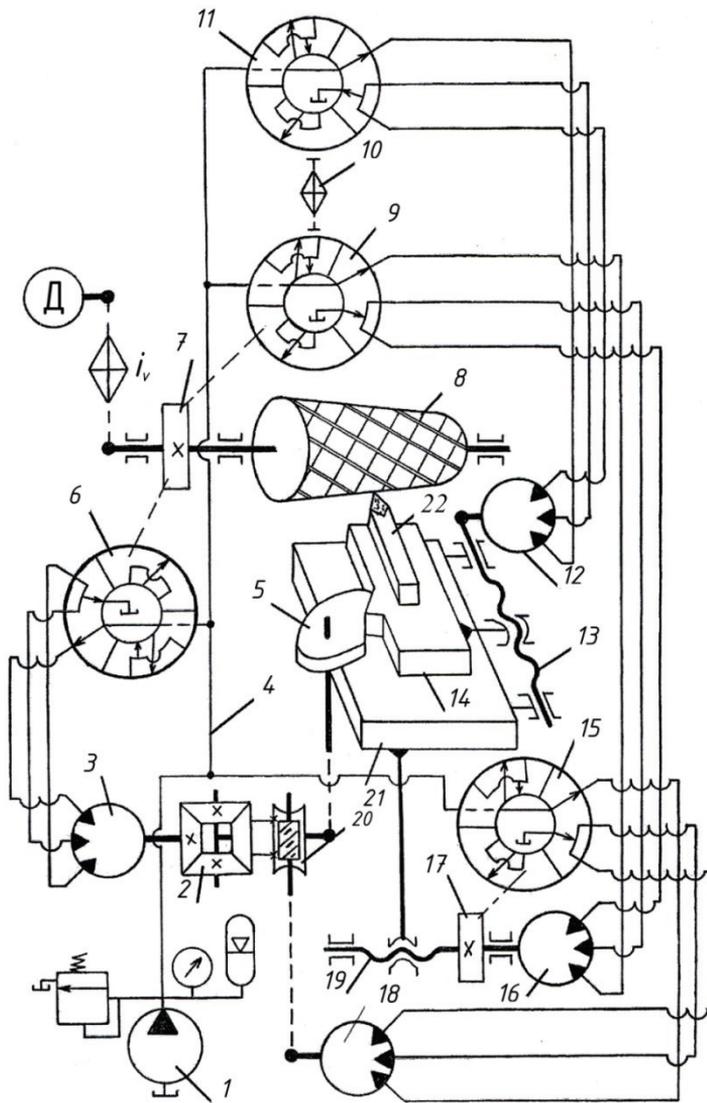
Структурная схема токарно-затыловочного станка с внутренними гидравлическими связями для обработки конических резьбовых изделий
